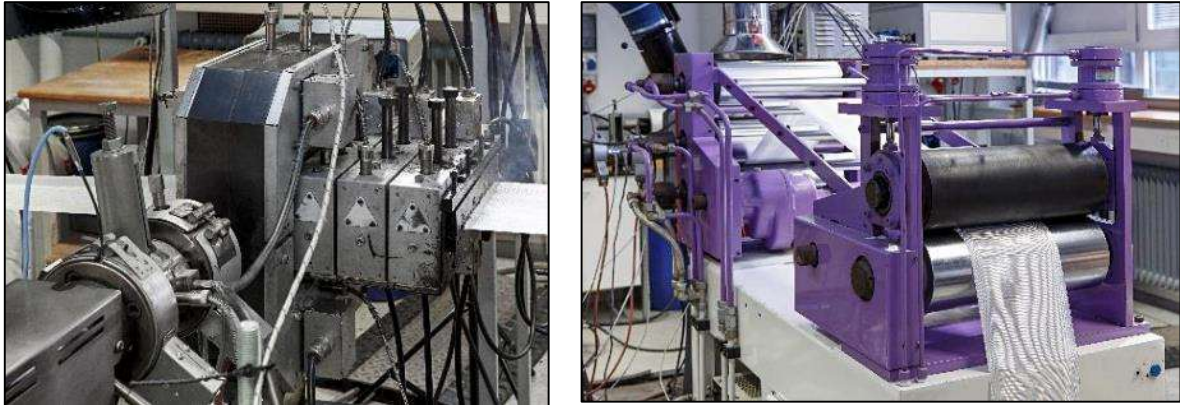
Fertigungsanlage am LBF für die Organosheets, Imprägnierwerkzeug (links) und Kalander (rechts)
